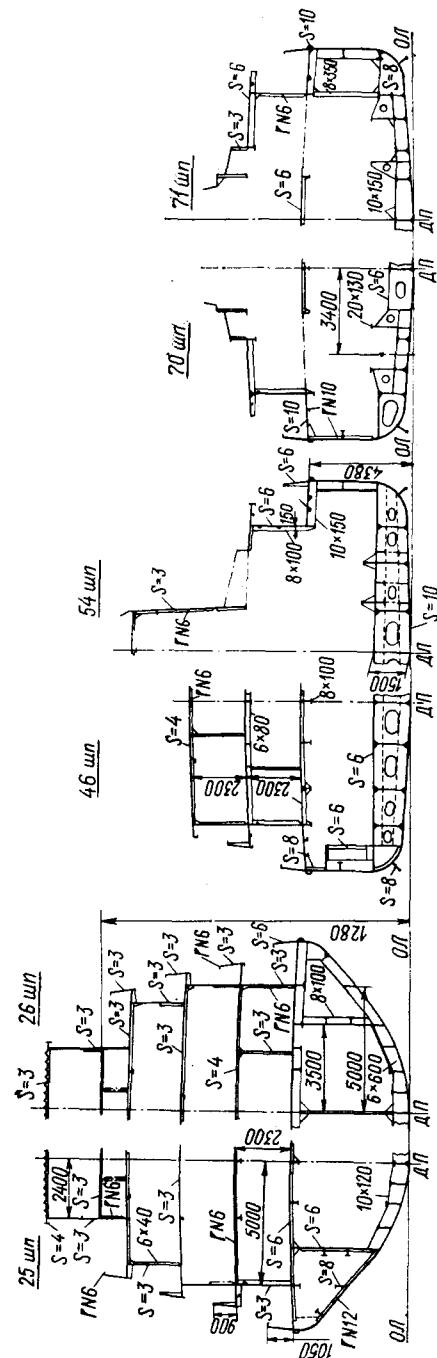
Конструктивные сечения корпуса толкача Маришал Блюхер.
